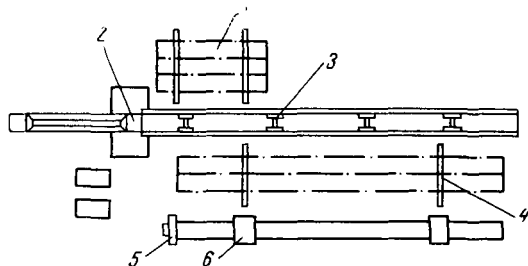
Механизированная трубосварочная линия (МТЛ) для наружной сварки поворотных стыков
